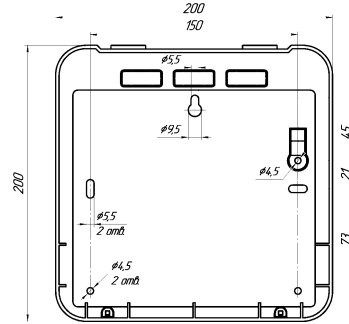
Розмітка отворів для кріплення корпусу модуля
